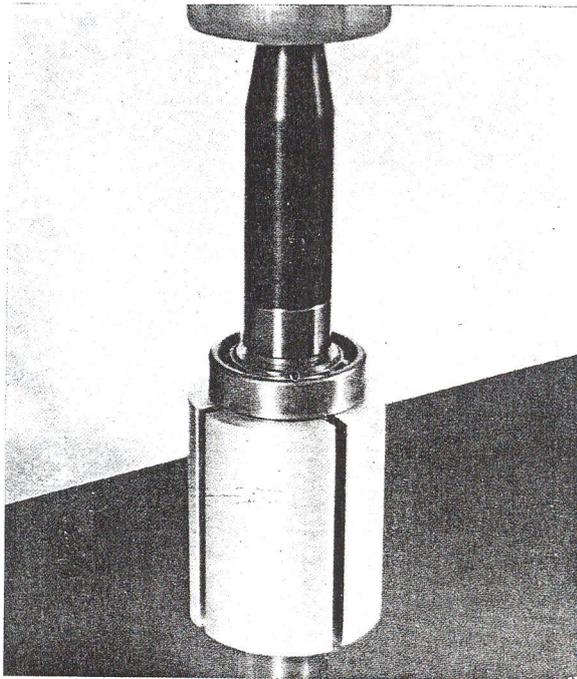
Montage du roulement sur l'arbre du rotor.
